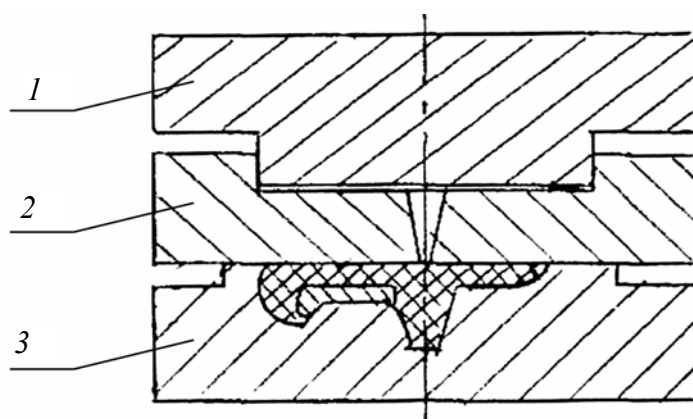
Пресс-форма компрессионно-литьевая:
